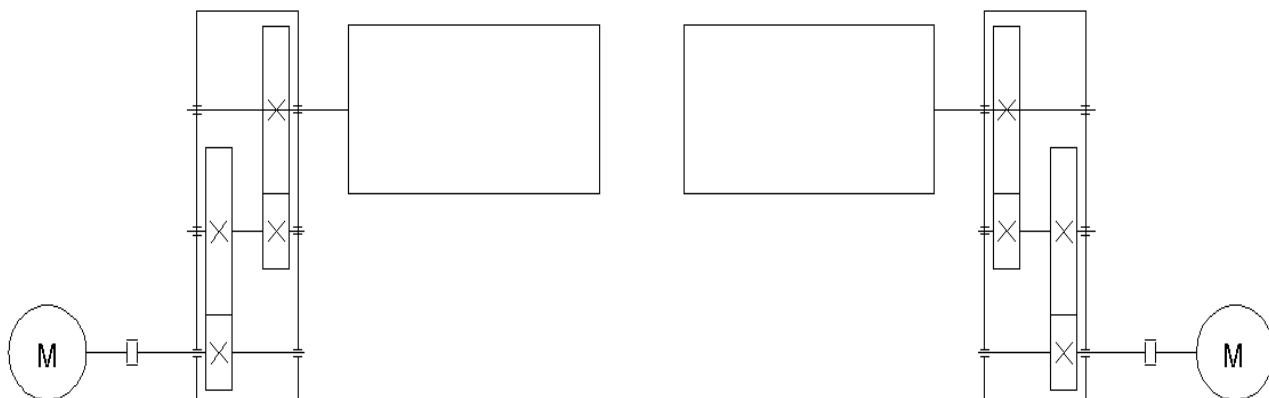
Кинематическая схема привода рамоподъема
